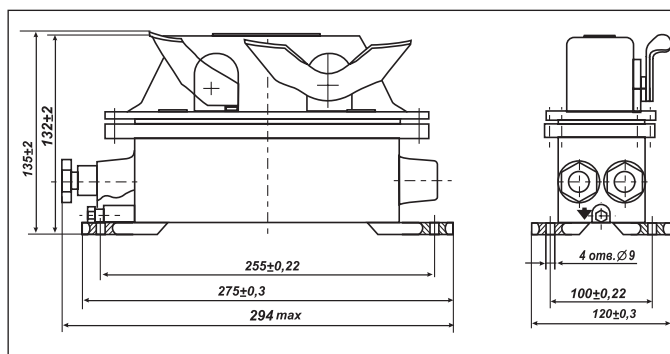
Габаритные и установочные размеры постов КУ123-32, КУ123-33
